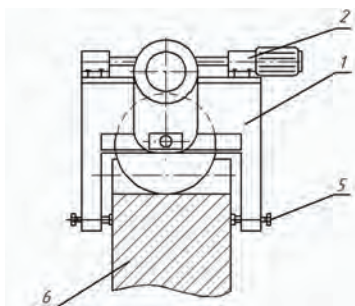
Приставной зубофрезерный станок – вид сбоку
